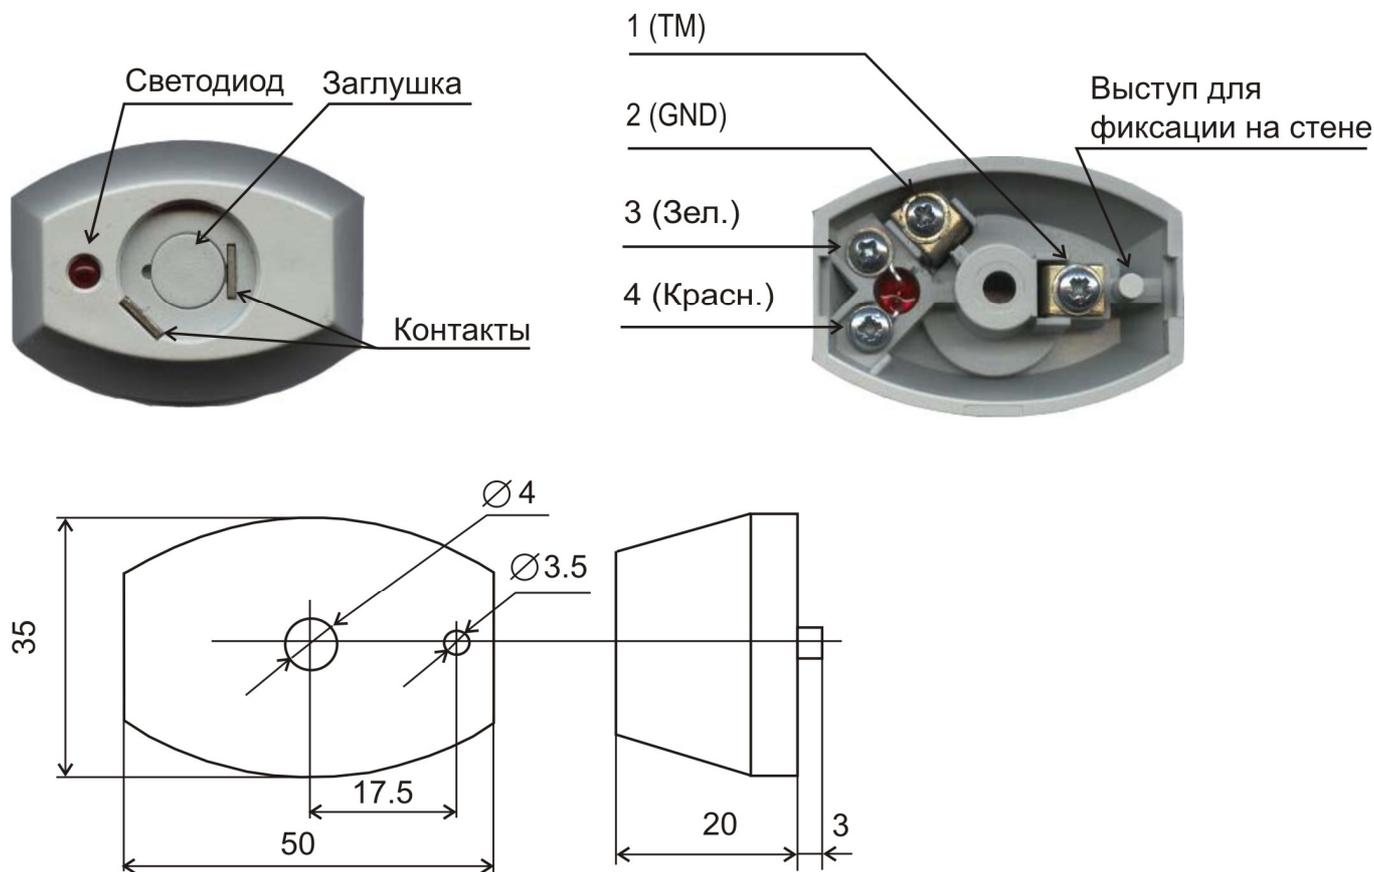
в. Внешний вид, габаритные и установочные размеры считывателя ключей «Touch Memory».
